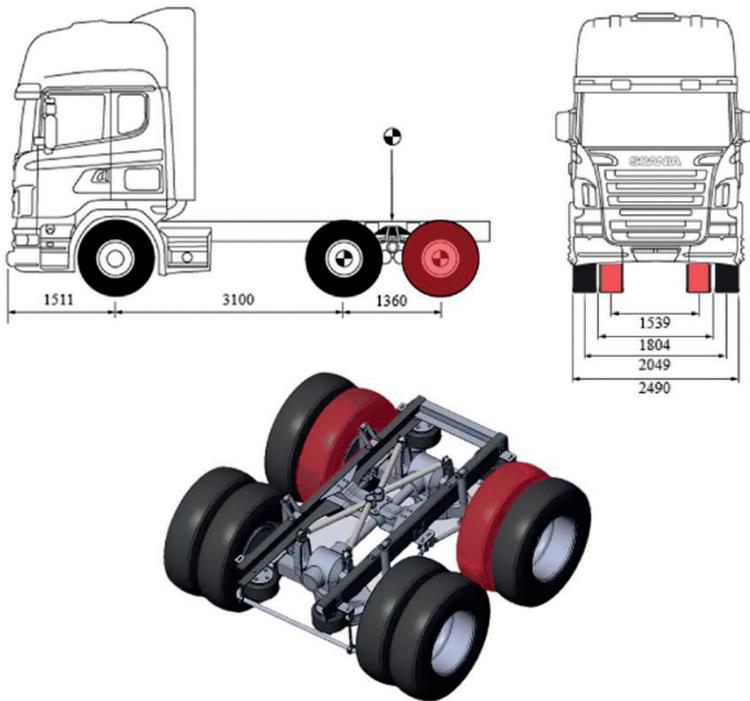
Размерная схема тягача SCANIA R500 и 3D-модель его задней тележки с отмеченными красным цветом наиболее загруженными колесами
